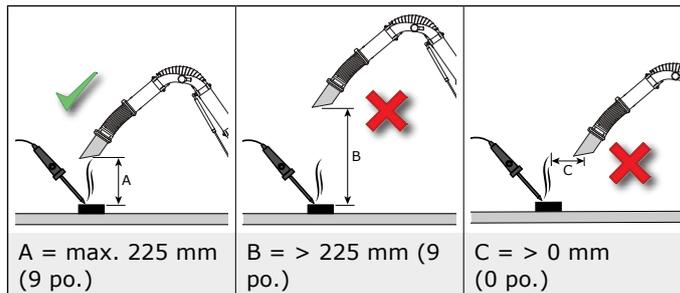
A = Position correcte de la buse (exemple : soudage)
